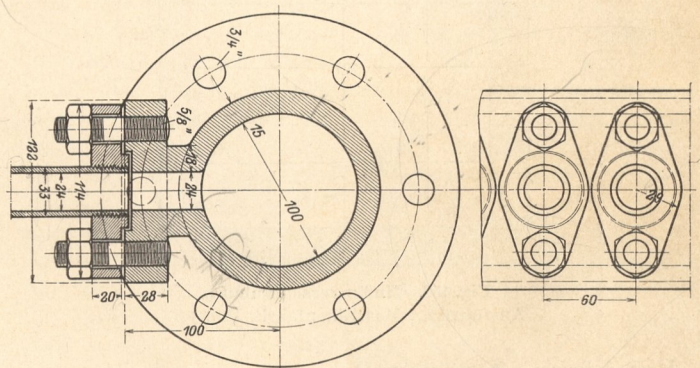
Flanschverbindung mittels Stiftschrauben.
